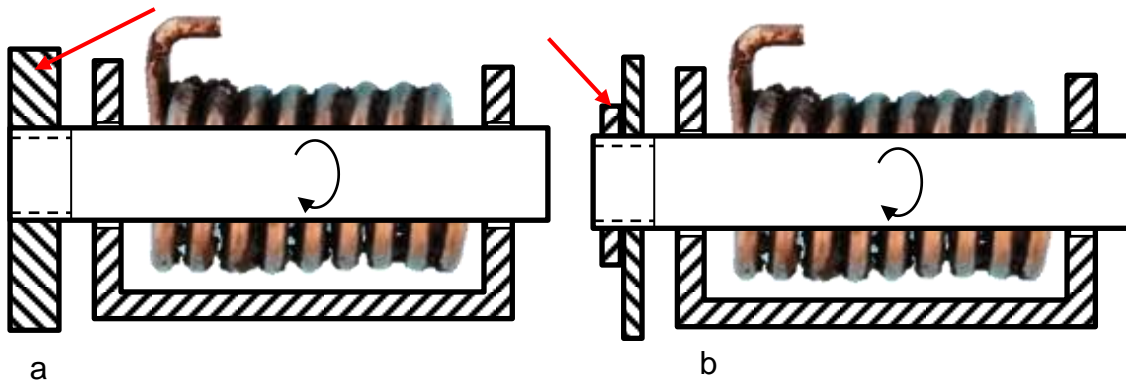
Eingeschraubte Drehbolzen: a) Im Magnetschenkel eingeschraubt und gegebenenfalls mit einer Kontermutter stabilisiert, b) In der Gewindebohrung eines stabilen Blechs, das an der Innenwand des Gehäuses angenietet ist, eingedreht.
